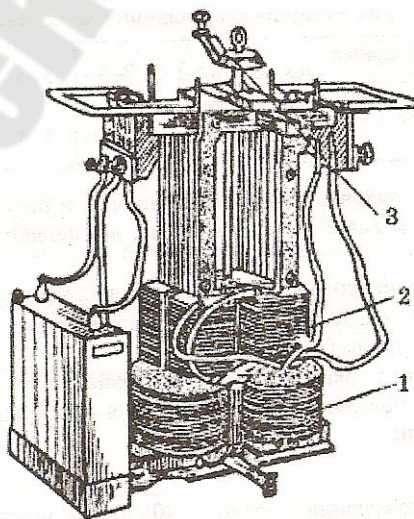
Сварочный трансформатор типа ТСК-500
